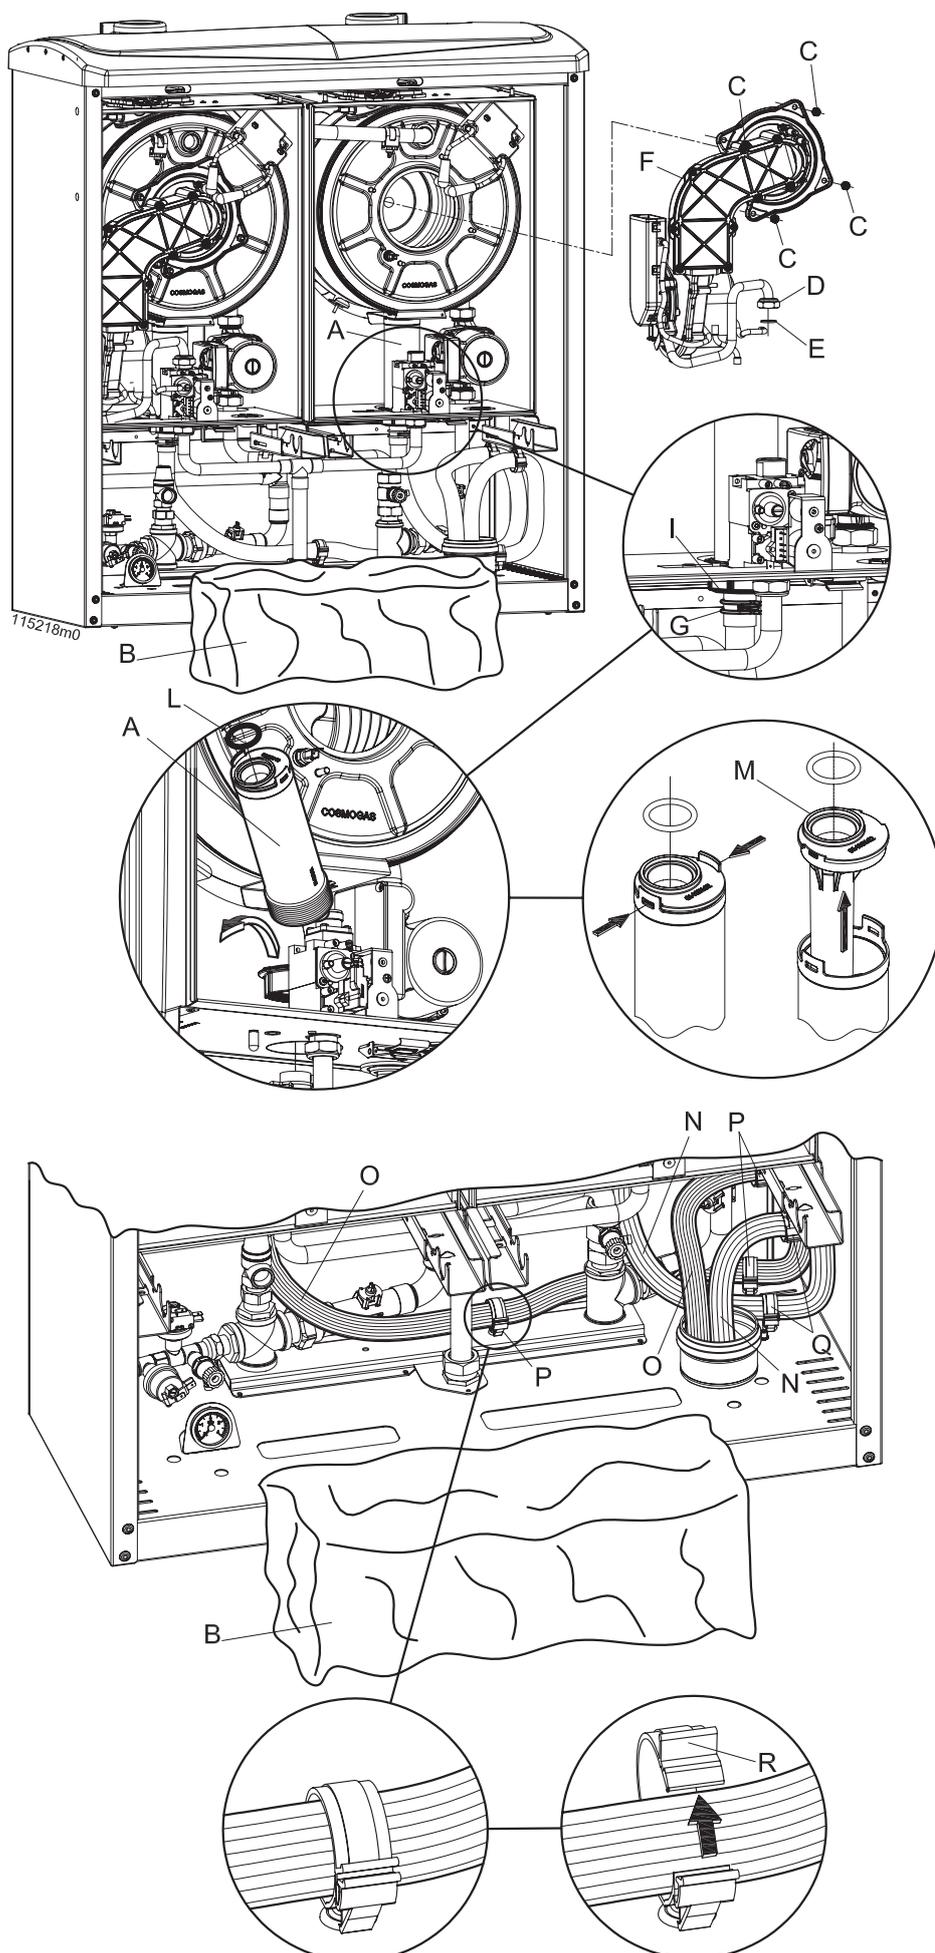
Montaggio e smontaggio della mantellatura e accesso ai componenti interni
